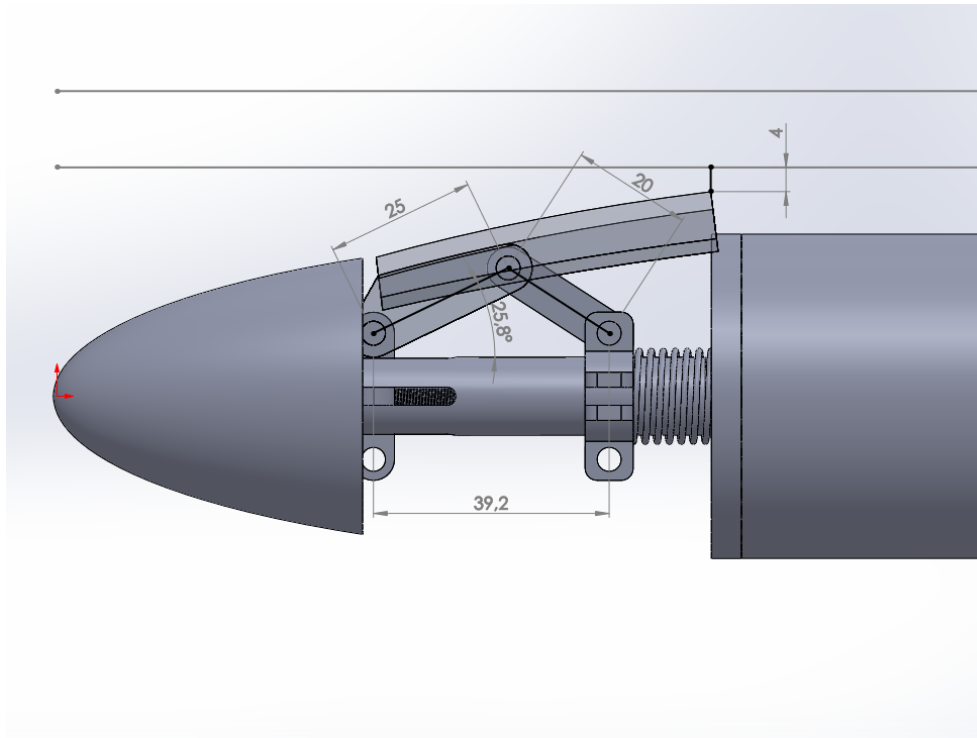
Vista de perfil com dimensões do sistema de elevação das pás para o caso de tubulação de 3 polegadas
